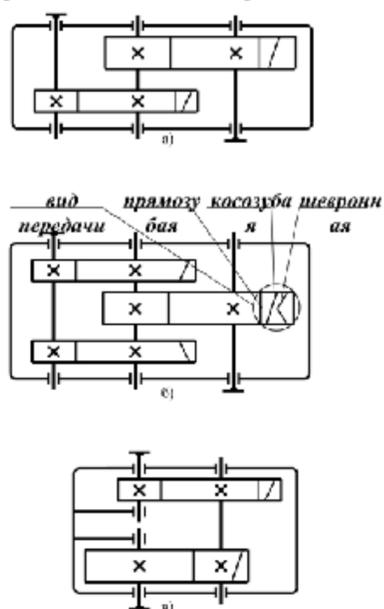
Наиболее распространенные кинематические схемы цилиндрических двухступенчатых редукторов
